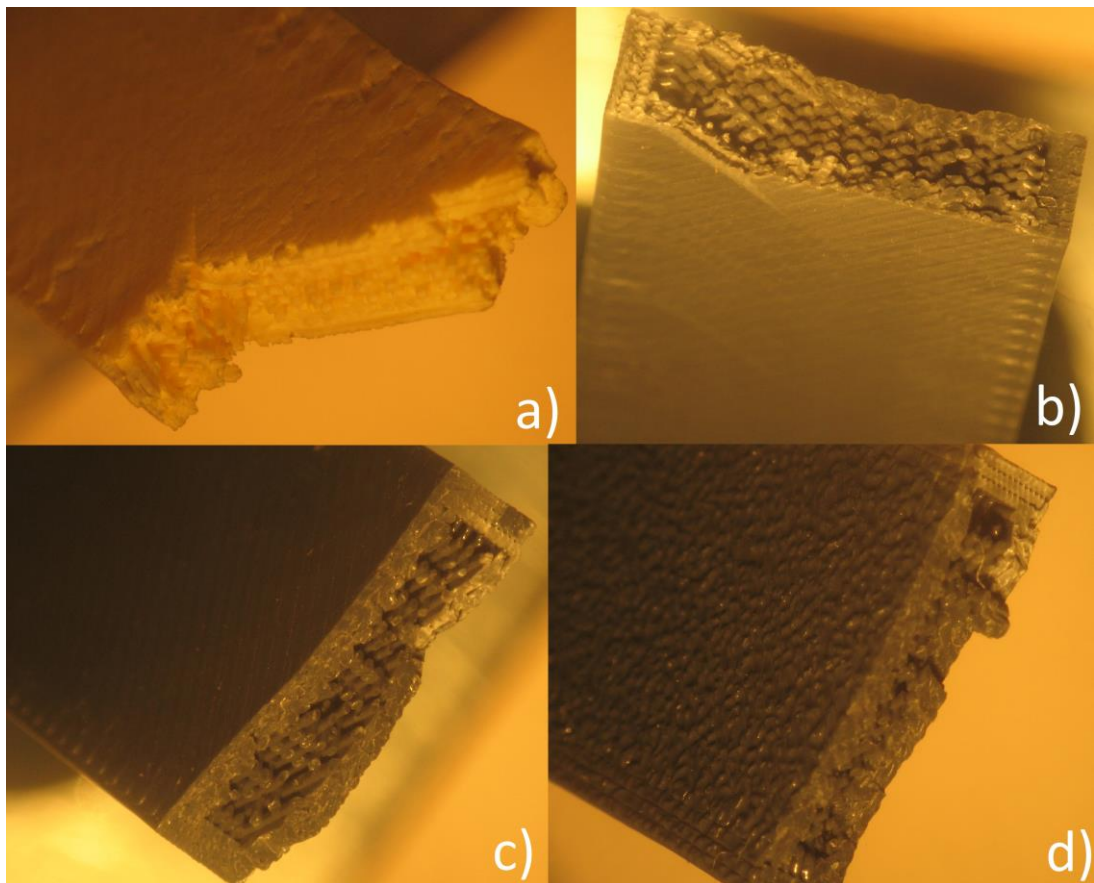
a) Superfície de rotura de provete de PLA virgem; b) Superfície de rotura de provete de PLA reciclado impresso a 220°C; c) Superfície de rotura de provete de PLA reciclado impresso a 237°C; d) Superfície de rotura de provete de PLA reciclado impresso a 255°C
